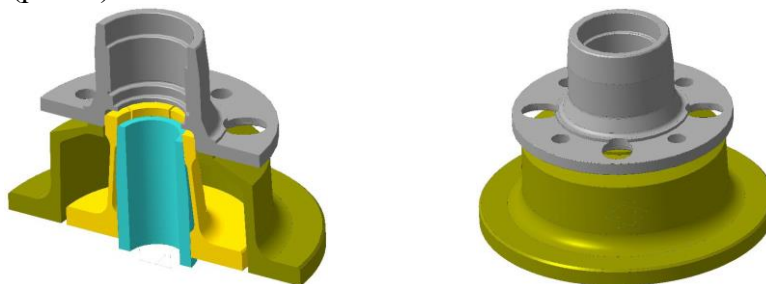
Твердотельная модель системы «приспособление-заготовка»
